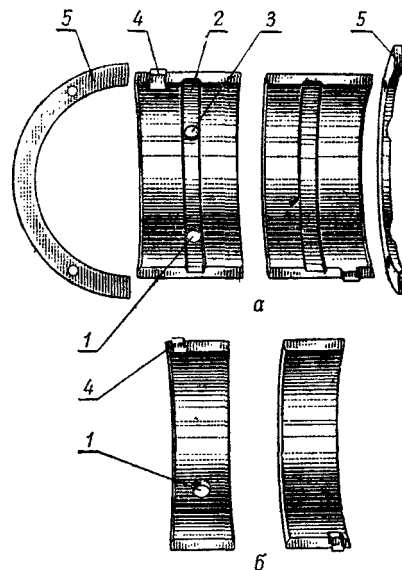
Вкладыши коренных подшипников дизеля СМД-14:
